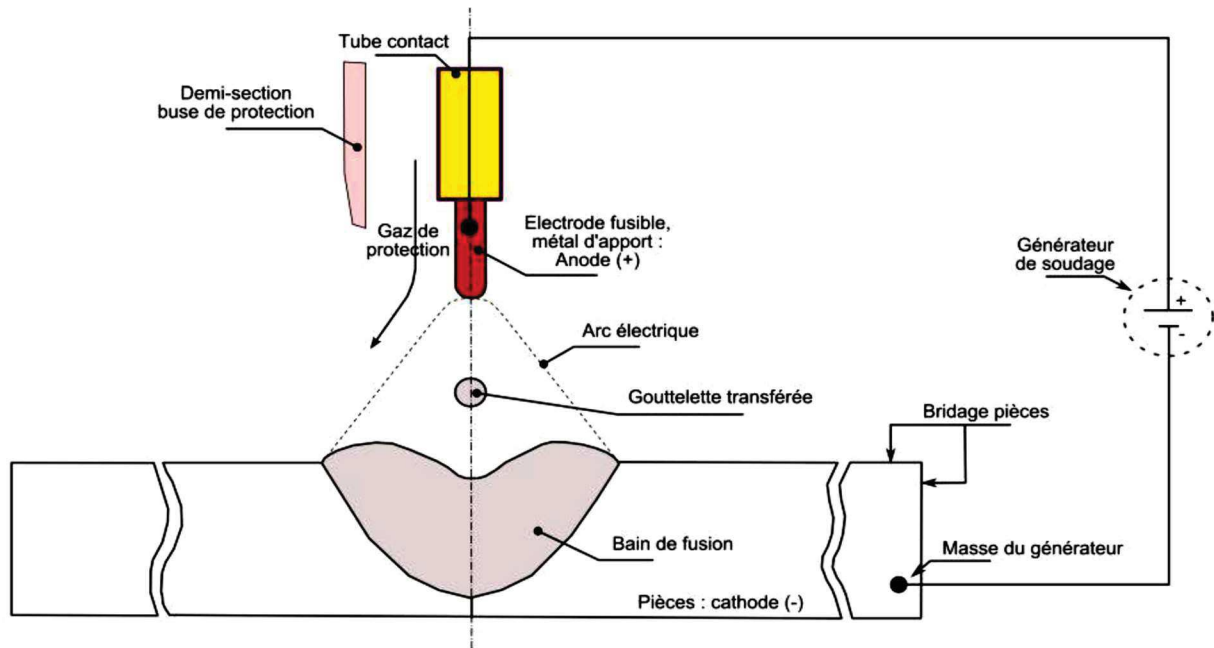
Principe du soudage MIG/MAG [33]
